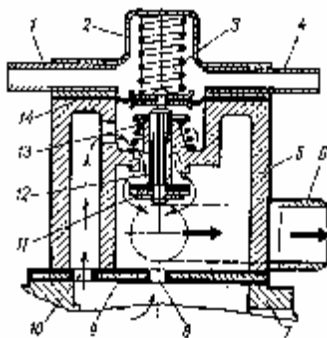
Дозирующе-экономайзерное устройство редуктора:
